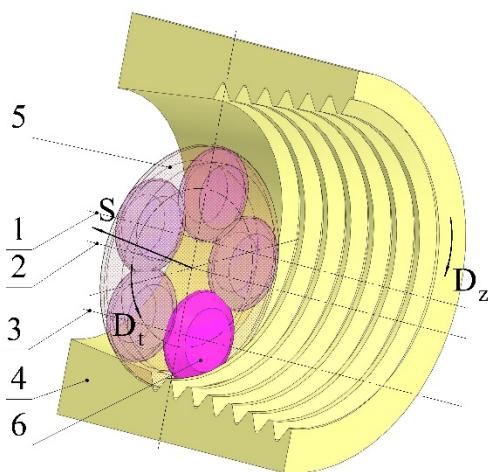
Схема формообразования внутренней конической резьбы накатыванием
